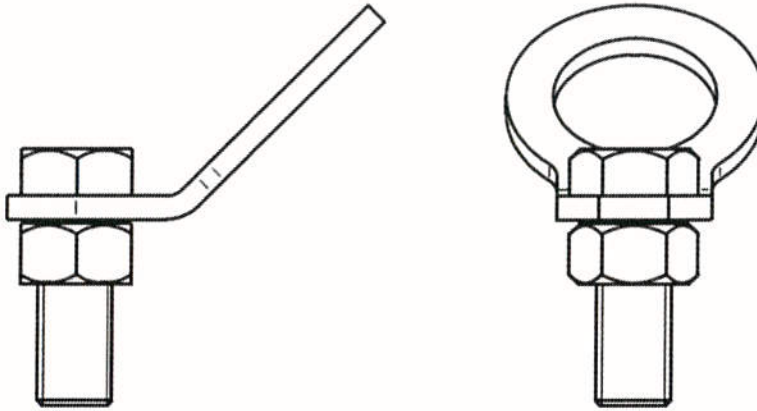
8: Anschlagseinrichtung, Typ: STABIL/STA-13
